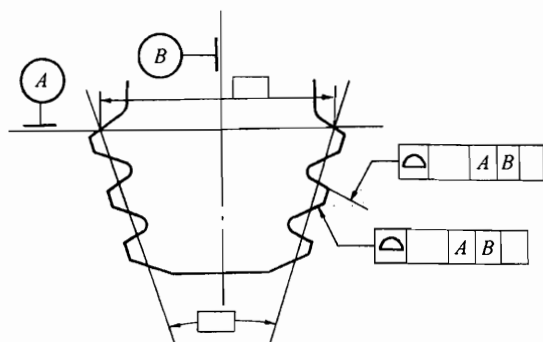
枞树形榫头形状公差用面轮廓度标注
